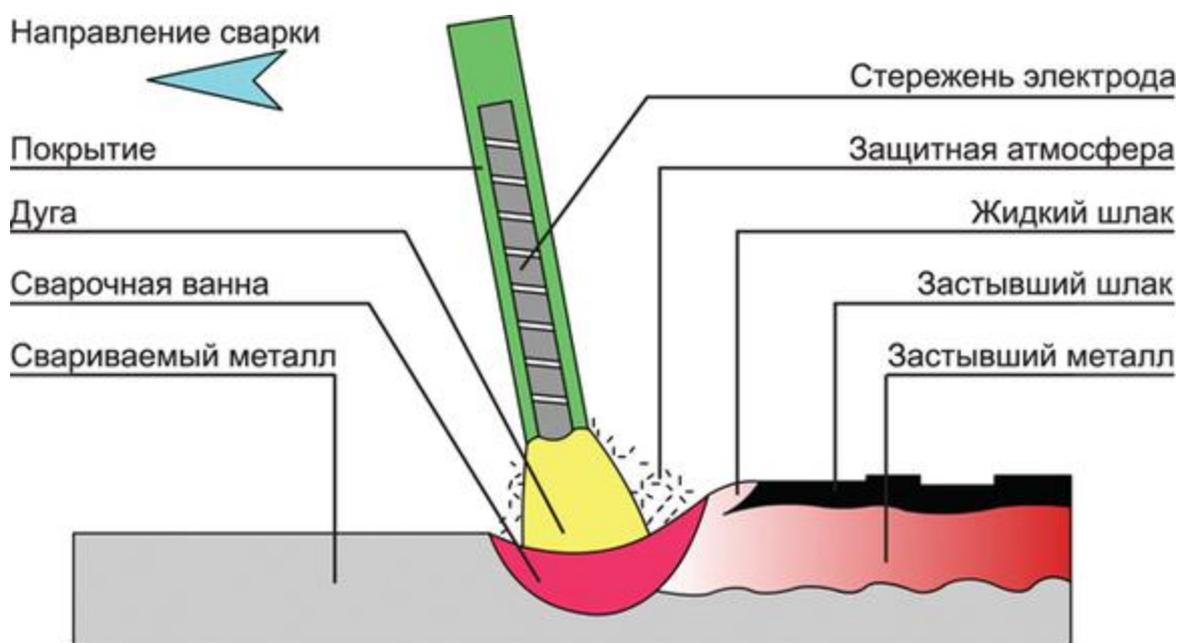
Дуговой сварки штучными электродами
